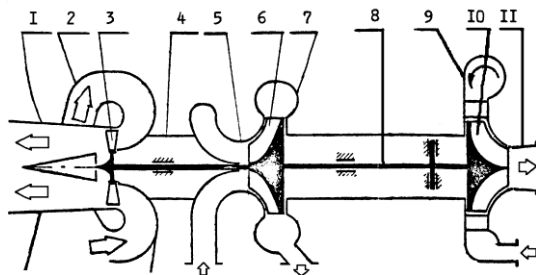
Принципиальная схема трёхколёсного турбохолодильника СКВ Ту-204: 1 – выхлопной патрубок вентилятора; 2 – входная улитка вентилятора, 3 - вентилятор; 4 – корпус турбохолодильника; 5 – входная улитка компрессора; 6 - компрессор, 7 – выходная улитка компрессора, 8 – ротор турбохолодильника; 9 - входная улитка турбины; 10 - турбина; 11 – выхлопной патрубок турбины
